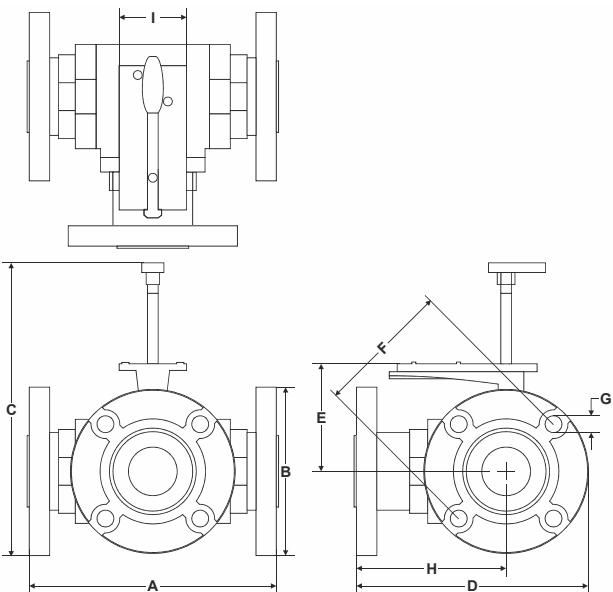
3-Wege-Ventile DN 80 Abmessungen
